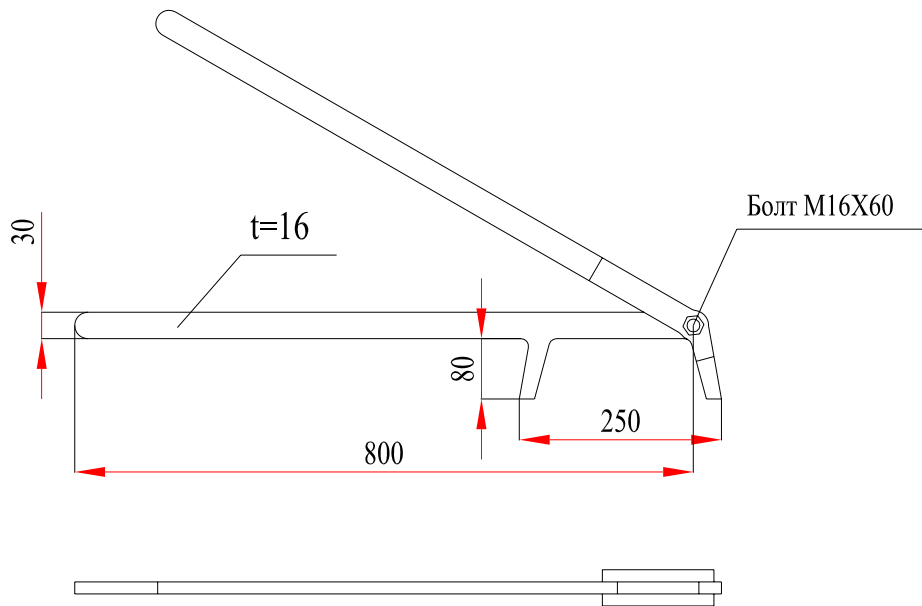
Приспособление для сборки трубы фундамента со стойкой анкерно-угловой и концевой опор
